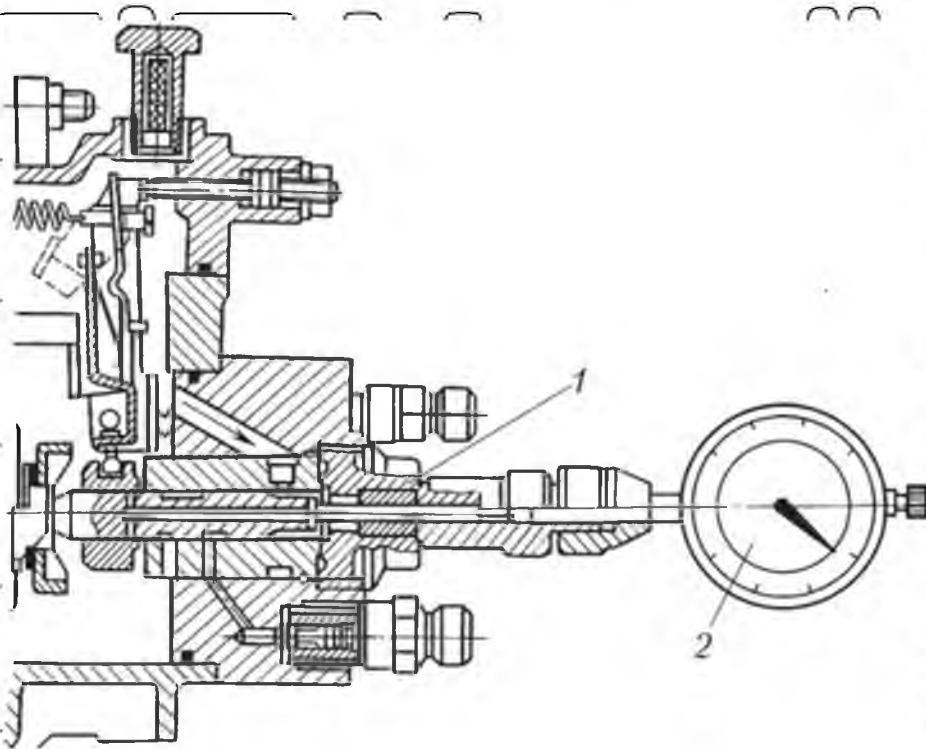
Встановлення індикатора для перевірки моменту початку упорскування для ГНВД фірми Bosch : 1 – отвір вивернутої центральної пробки; 2 - індикатор
